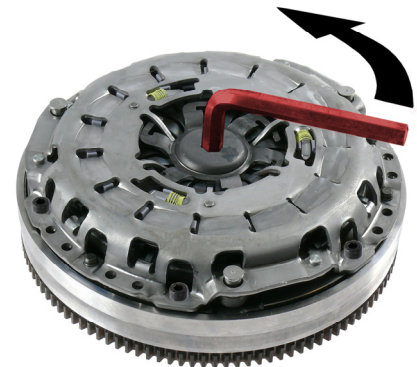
Verriegelungsstück herausdrehen / Unscrew locking piece / Retirer la pièce de verrouillage en tournant / Desenroscar la pieza de bloqueo / Rimozione dell'elemento di bloccaggio
